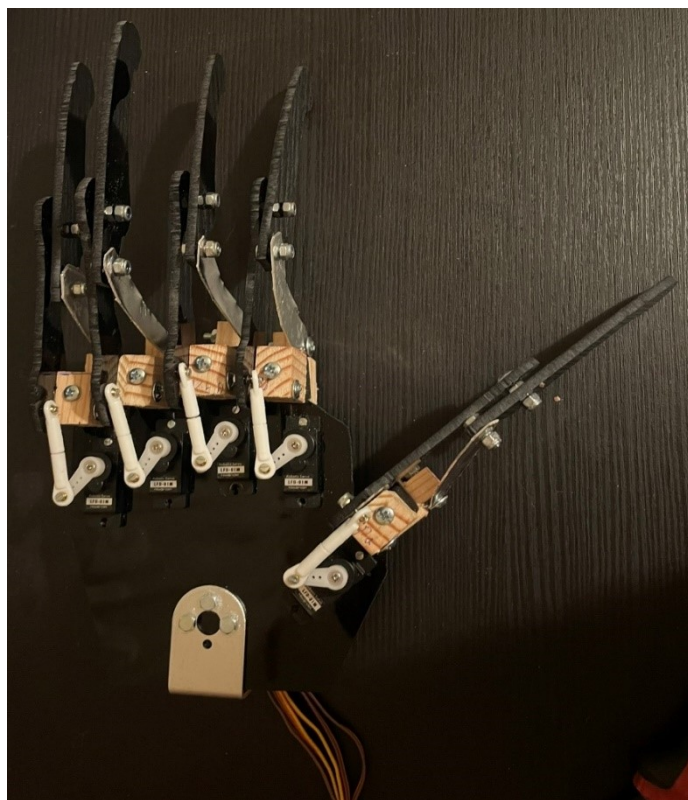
Vizualizace dílů pro ohyb prstu
